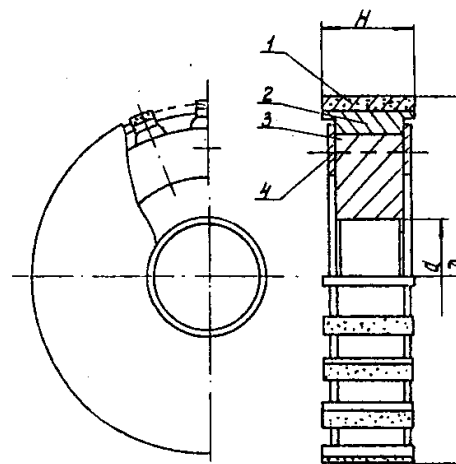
Общий вид алмазной цилиндрической фрезы:
